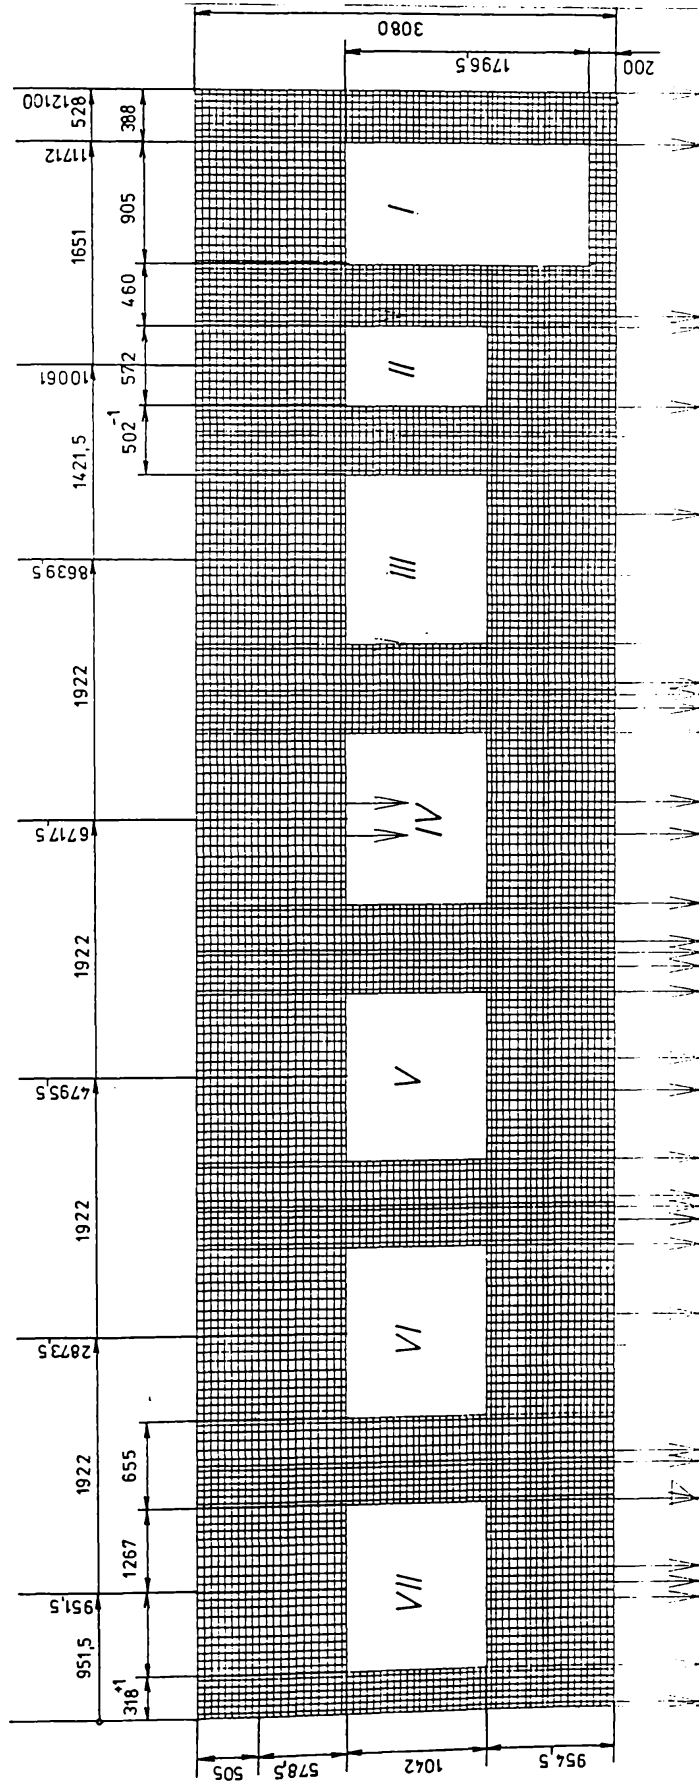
Structura plană a vagonului - varianta de calcul - V.P.P.1.
